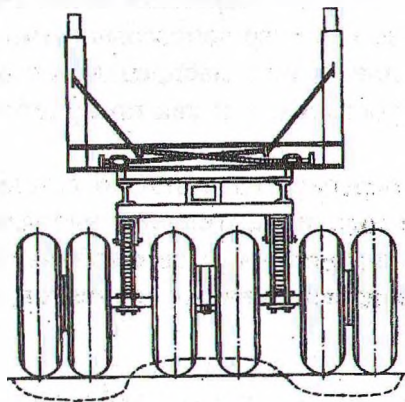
Конструкция прицепа-ропуски (вид сзади)
